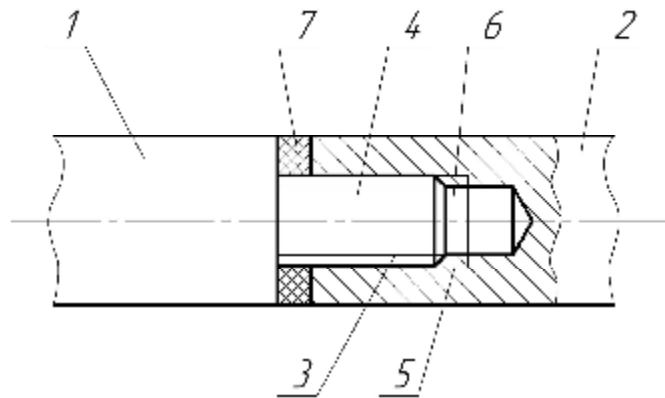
Схема різьбового з'єднання валів з фрикційною шайбою
